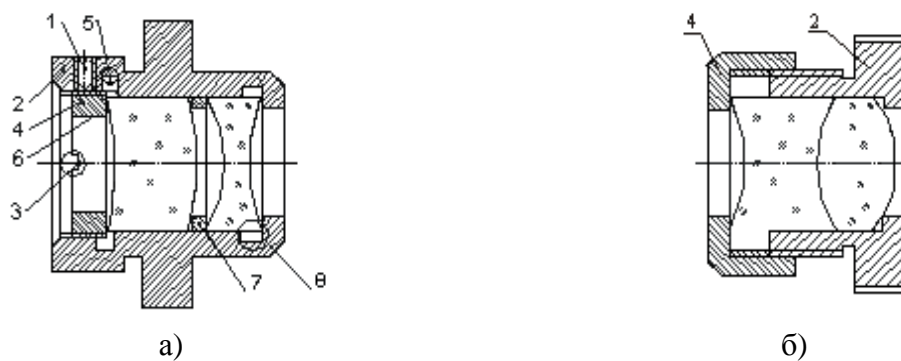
Кріплення різьбовим кільцем: а – внутрішнє кільце; б – зовнішнє кільце; 1 – установочний гвинт (оберігає від відгвинчування); 2 – корпус (оправа); 3 – шліць; 4 – різьбове кільце; 5 – технологічна проточка (що оберігає край лінзи від руйнування); 6 – виступ краю лінзи за посадочну поверхню (для надійного кріплення кільцем при негативному допуску на товщину лінзи); 7 – проміжне кільце; 8 – оберігання краю лінзи від руйнування
